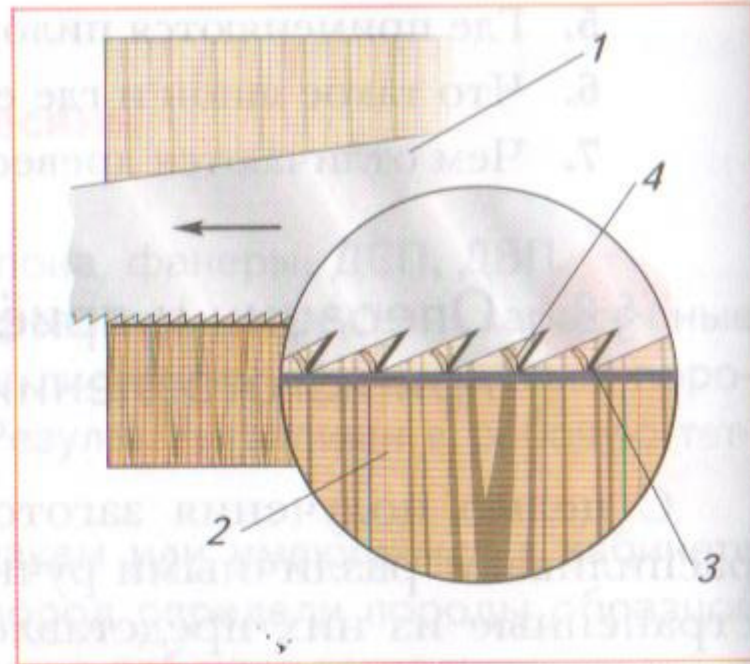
Продольное пиление древесины: 1 — пила; 2 — заготовка; 3 — режущая кромка и вершина зуба; 4 — опилки
